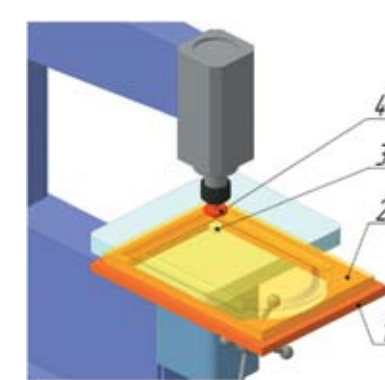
Фрезерование по копиру: 1 – плоский копир, 2 – заготовка (показана условно-прозрачной), 3 – упор в столе, 4 – фреза
